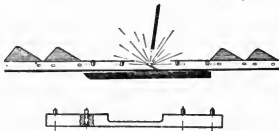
Сварка спинки ножевой полосы на кондукторе.
